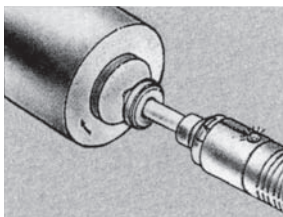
Stirnseitige Drehzahlmessung mit Kontaktadapter.
